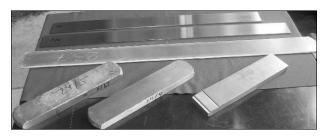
Заготовки пластин гафния после ковки, после механической обработки поверхности; прокатанная полоса, а также шлифованные и обрезанные пластины
